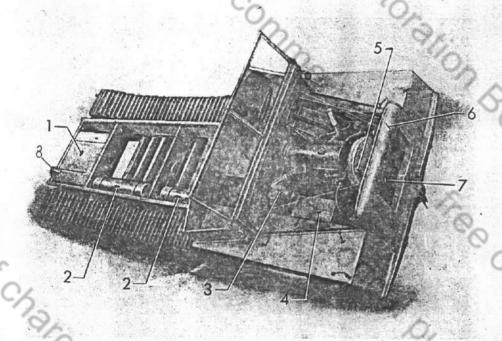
Schwerer Wehrmachtschlepper, sWS, Fahrgestell, Ansicht von oben
